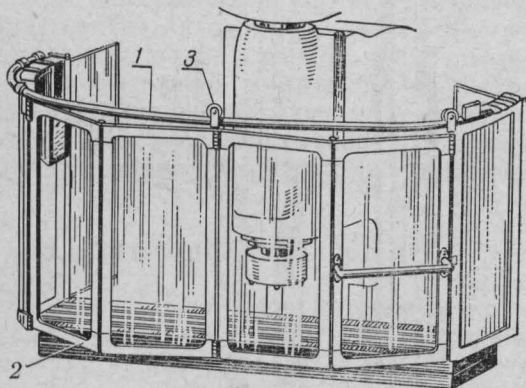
Ограждение системы ЛЮТ ВЦСПС для фрезерного станка.
